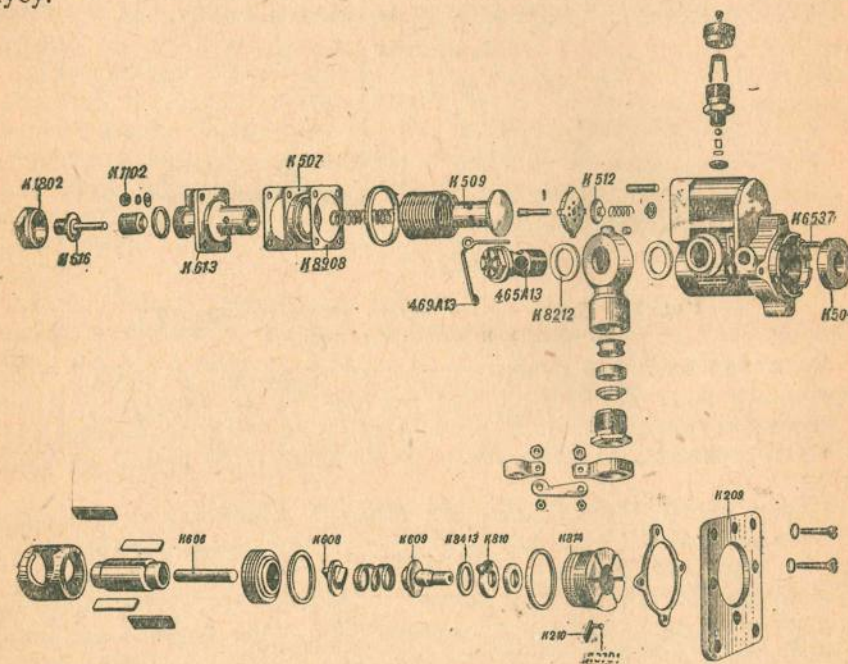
Топливный насос БНК-6 (в разобранном виде)
